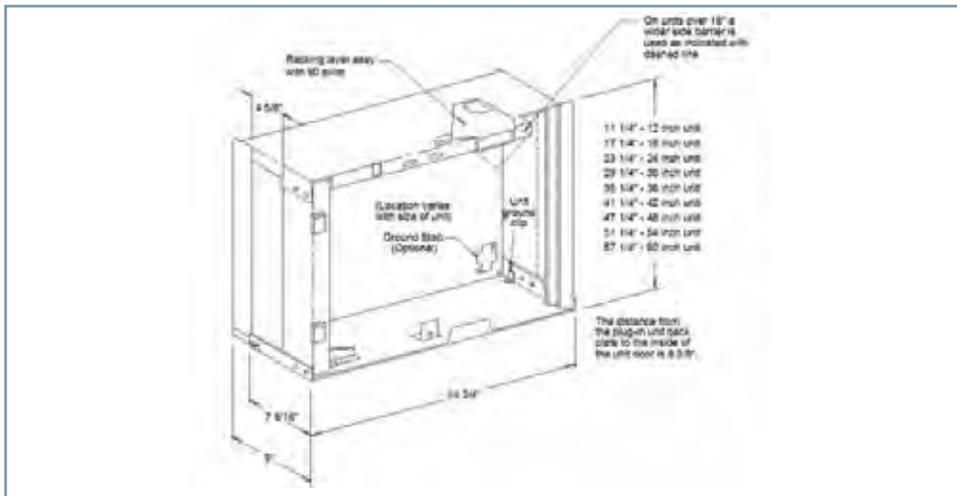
Vista isométrica de unidad extraíble con dimensiones
